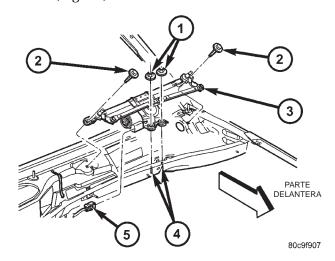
Desmontaje e instalación del módulo de limpiador delantero
